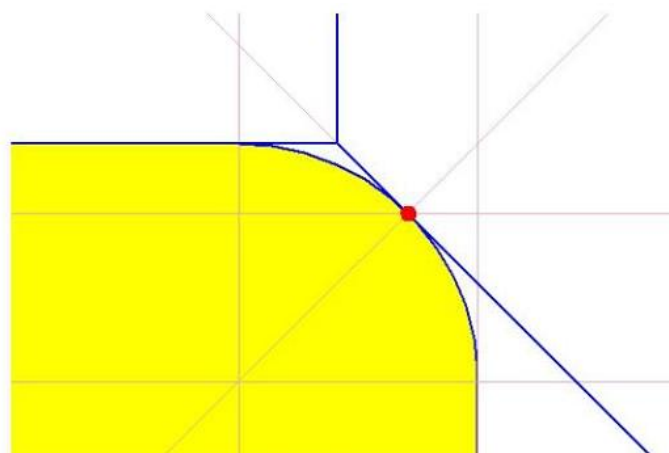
Потрібне положення різця для обробки канавки
